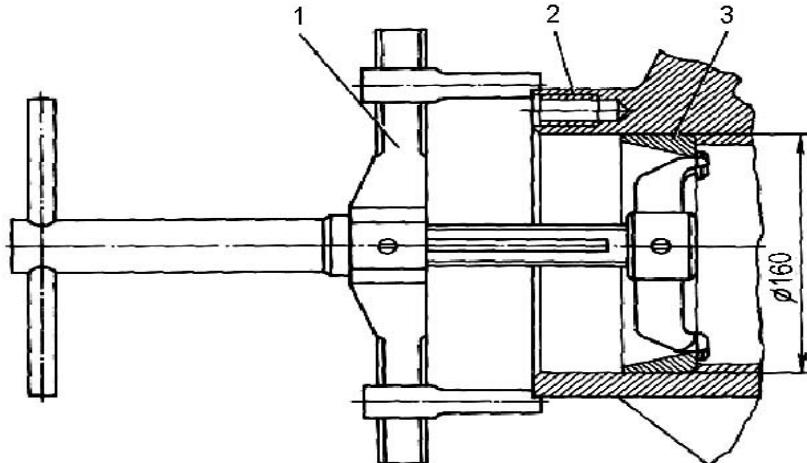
Выпрессовка наружных колец подшипников ступиц:
